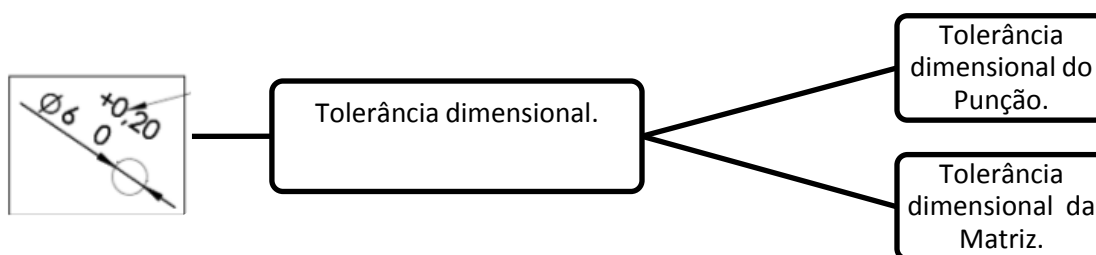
Processo de determinação da tolerância dimensional do furo B.
